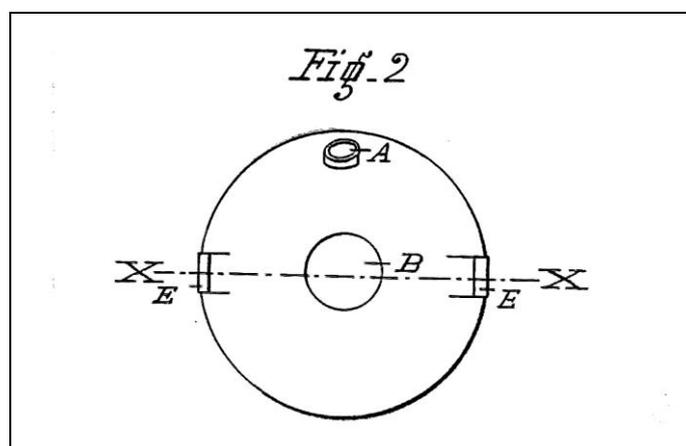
Detalle superior (Arch. J.M. Sanchis)
